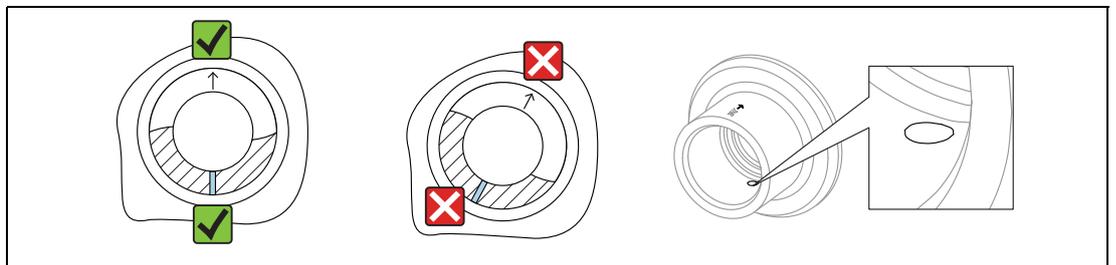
Einschweißadapter mit Leckagebohrung
